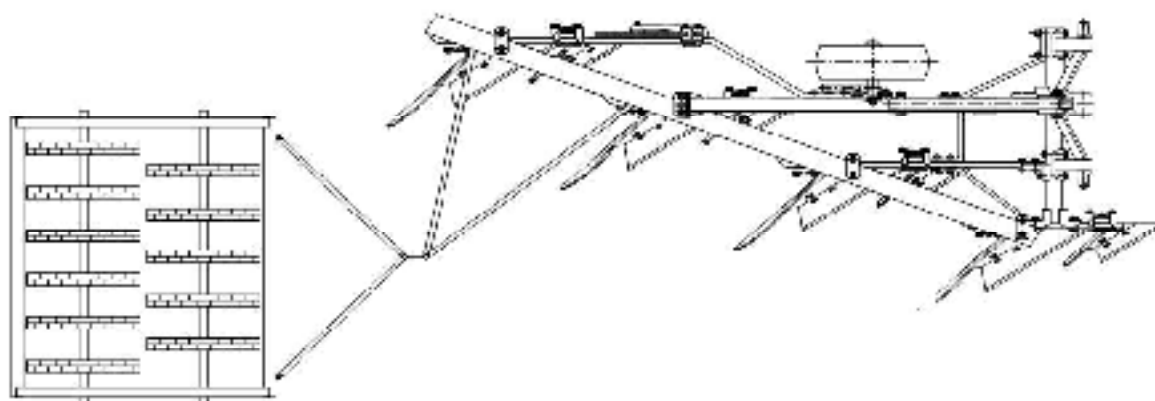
Комбинированный пахотный агрегат с кольчато-шпоровыми катками.
